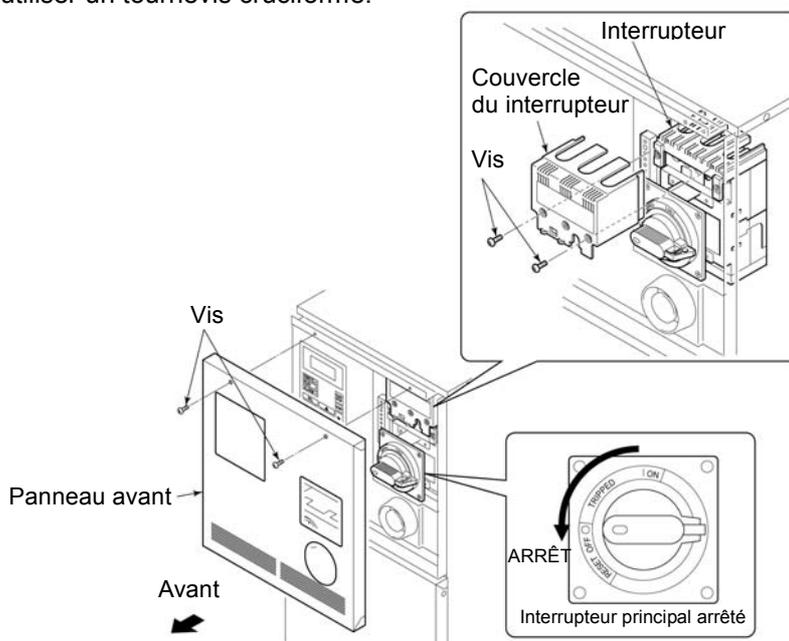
Interrupteur principal arrêté et dépose du panneau avant/couvercle du interrupteur
